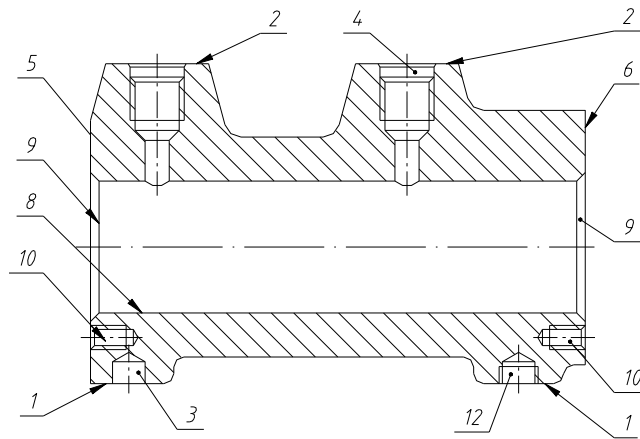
Ескіз деталі «Корпус гідропідсилювача ПЕА 01.105»
